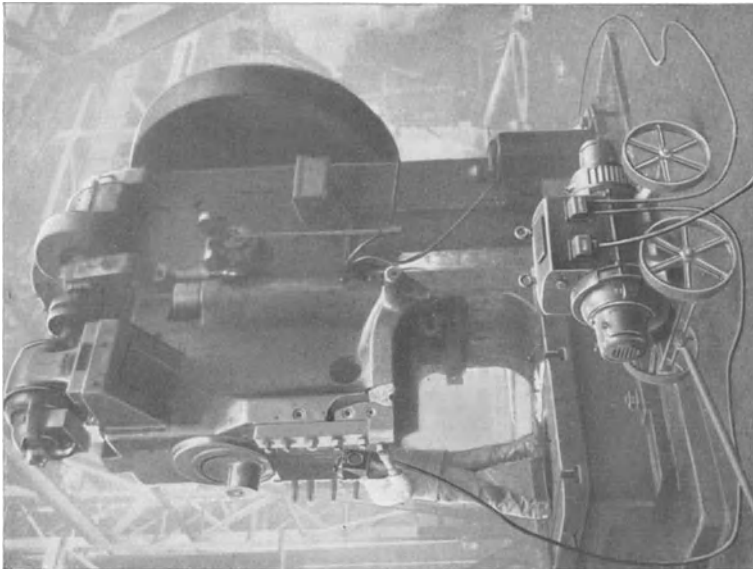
Exzenterpresse während der Schweißung.
